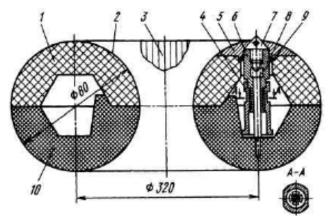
Конструктивная схема вымываемой песчаной оправки торовой формы с закладными элементами штуцера оболочки и цанговым устройством для извлечения штуцера из оправки после намотки однонаправленного КМ: 1, 10 - верхняя и нижняя половины торовой оправки; 2 - поверхностный слой из пленки ПВС-Э; 3 - схема укладки ленты, вырезанной из пленки ПВС-Э; 4 - штуцер; 5 - втулка; 6 - разжимная цанга; 7 - раздвижной конус; 8 - фторопластовое уплотнение; 9 - установочный винт
